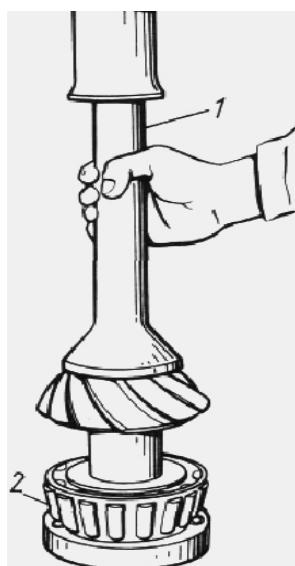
Напрессовка внутреннего кольца заднего подшипника на вал:
